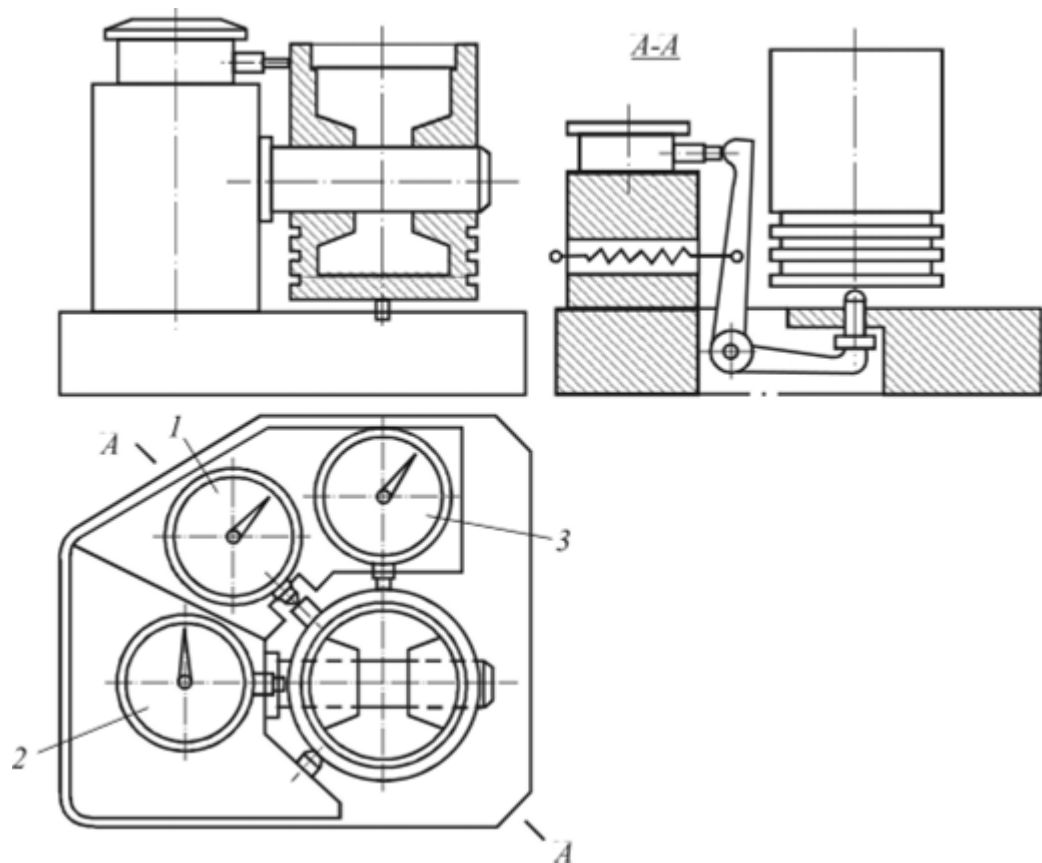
Багатовимірний контрольний пристрій для перевірки поршня
